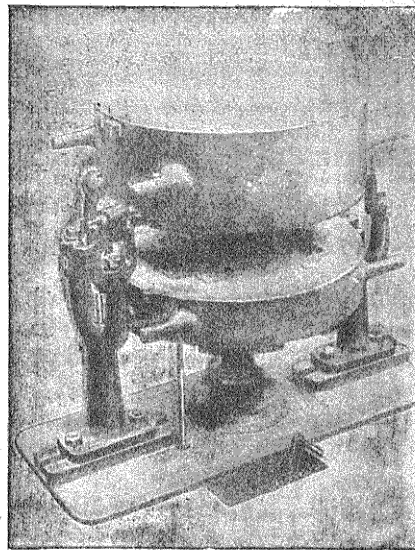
Machine à assembler et à démotter. — Position d'assemblage.
